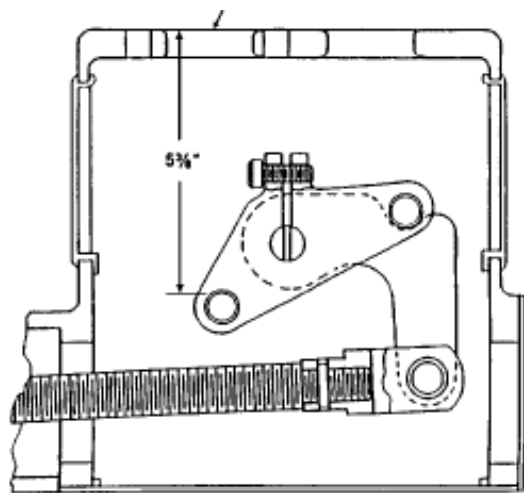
Ensamblaje general del actuador, tamaños de actuador B y C
